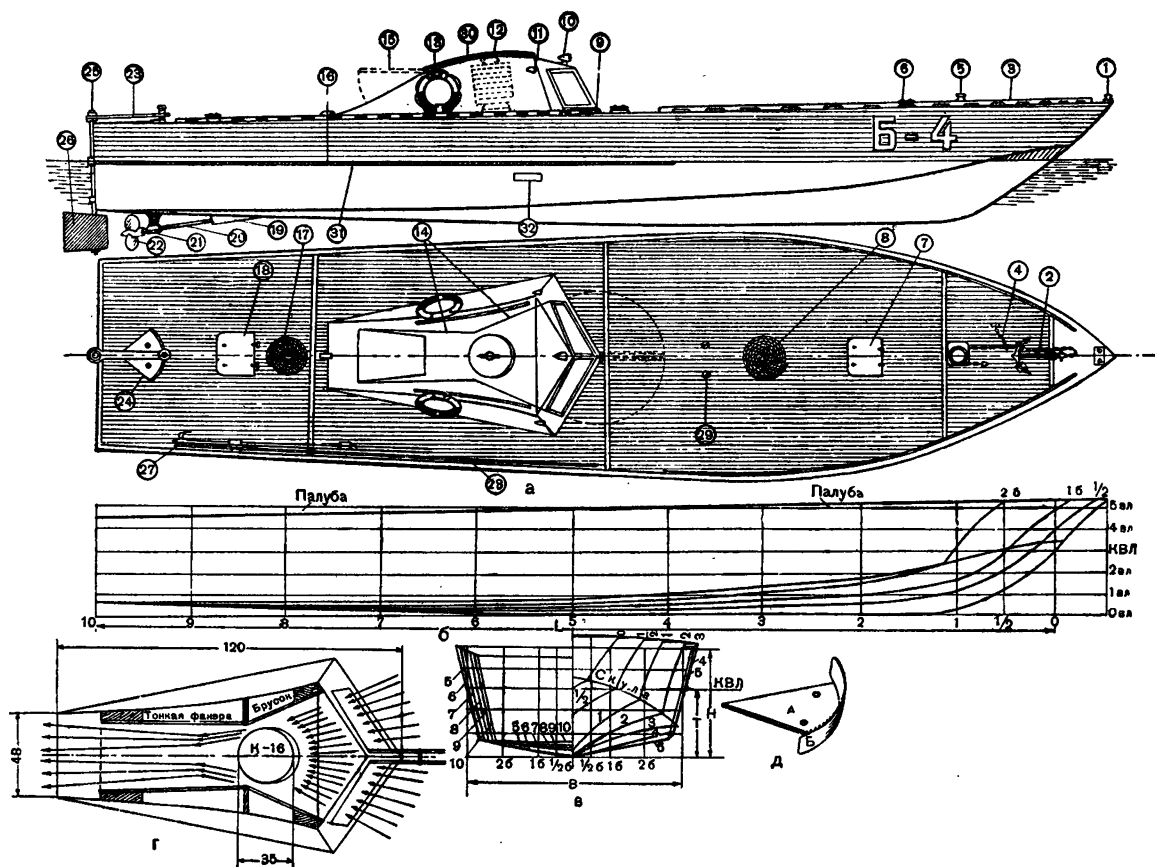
Общий вид и теоретический чертеж модели спортивного катера.
